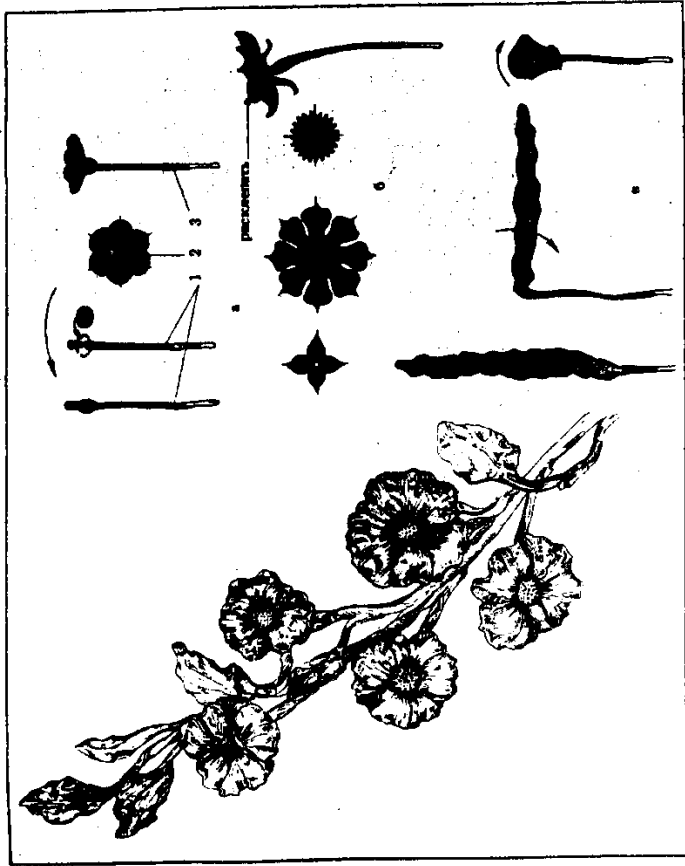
Изготовление сборных однолучных и многолучных цветов: а — шпорец (1 — стержень с утолщением на конце, 2 — розетка, 3 — цветок в сборе); б — шпорец; в — роза (из распыленной и скрученной проволоки)
